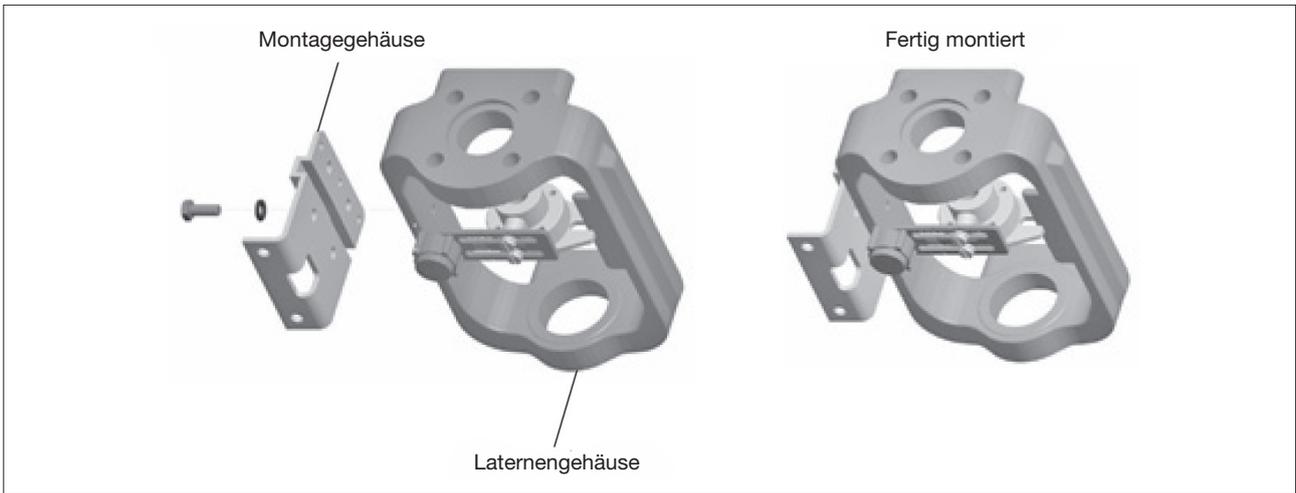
Montage Montageplatte an Linearantriebe mit Laterne
